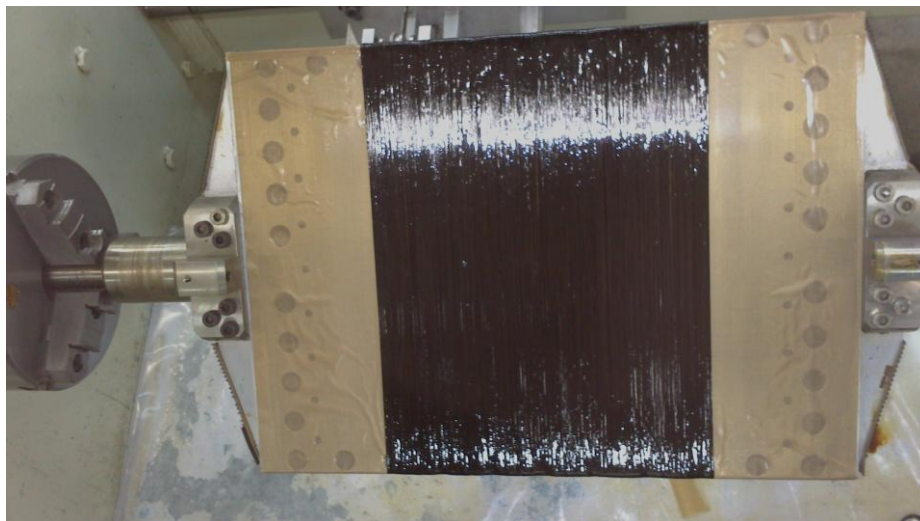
placa de fibra de basalto fabricado por uma técnica de enrolamento filamentar.
